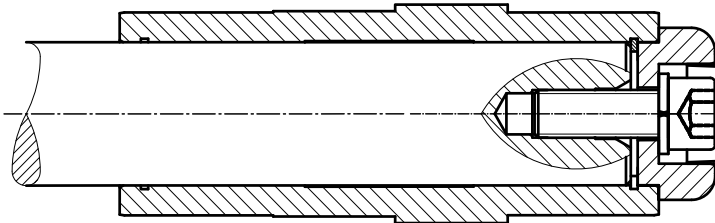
Getriebe auf Welle ohne Anlageschulter mit Befestigungselement befestigt
